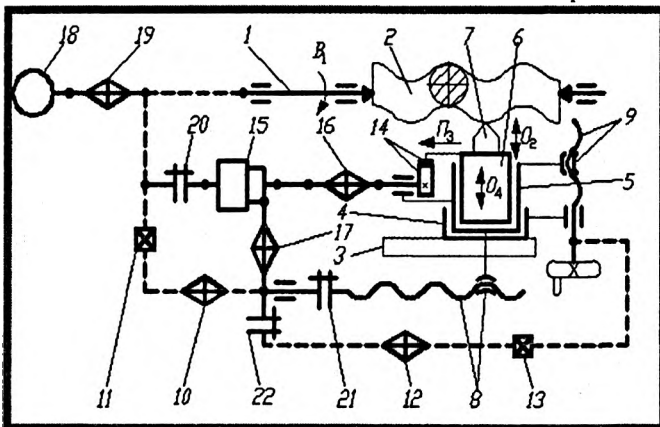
Структурная схема станка для обработки круговых винтовых поверхностей
